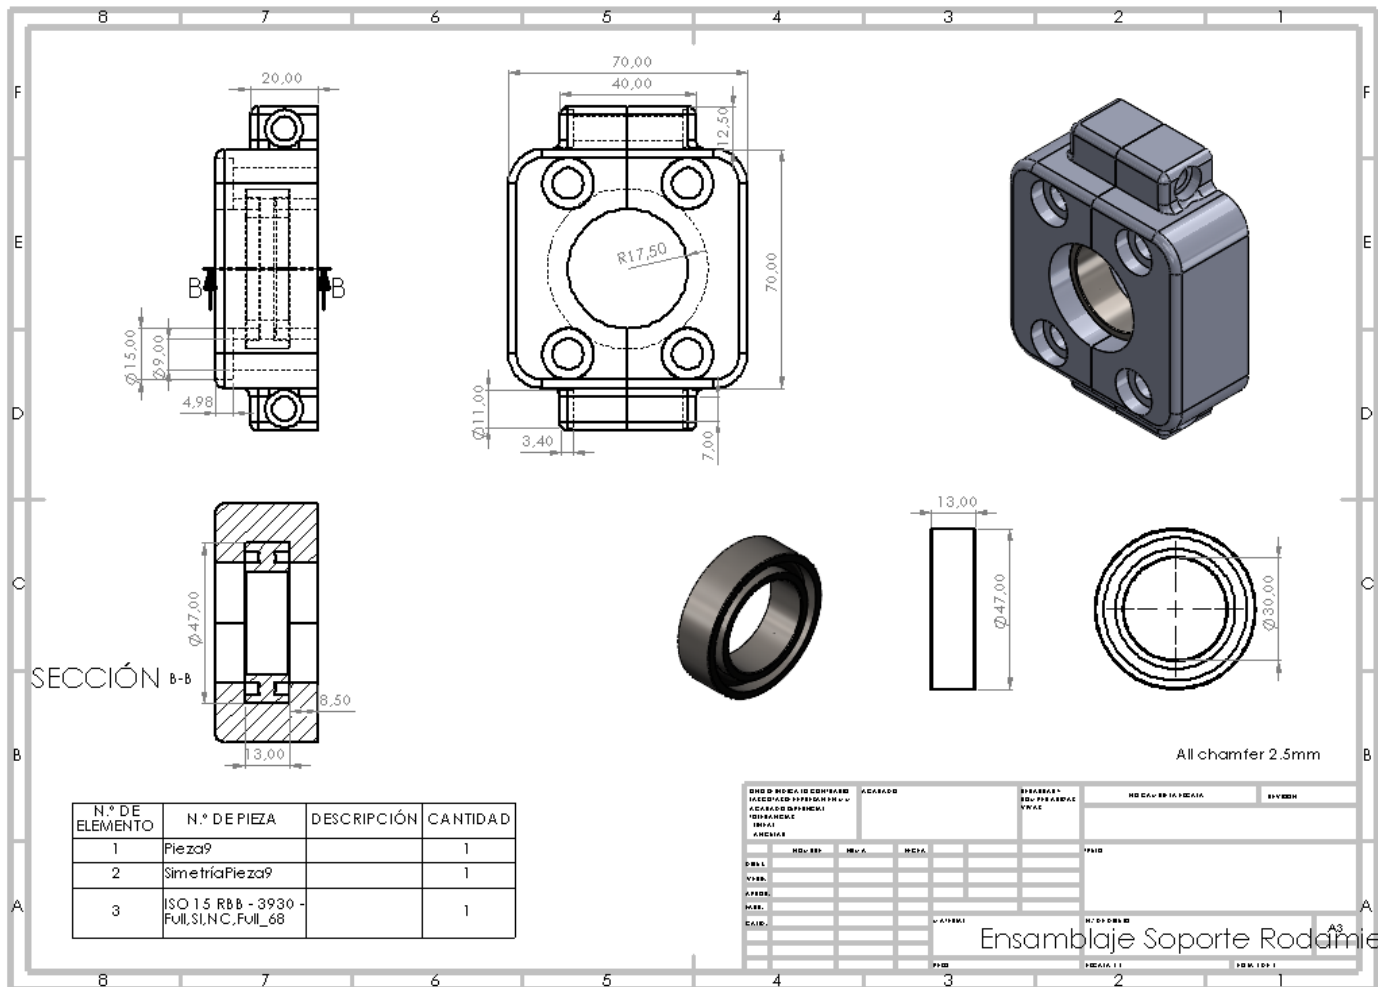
Ensamblaje Soporte Rodamiento Anclaje Motor Principal
